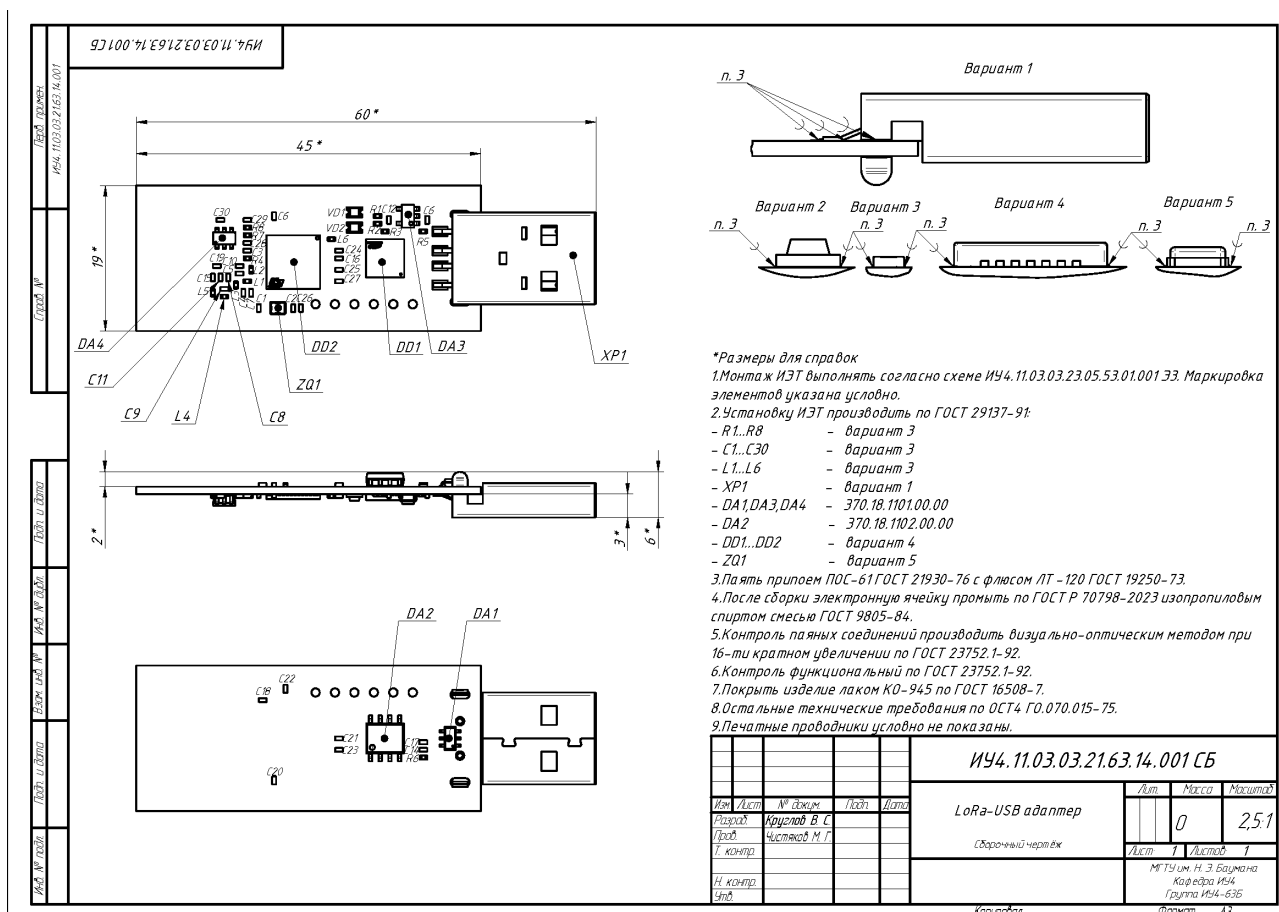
Часть сборочного чертежа печатной платы
